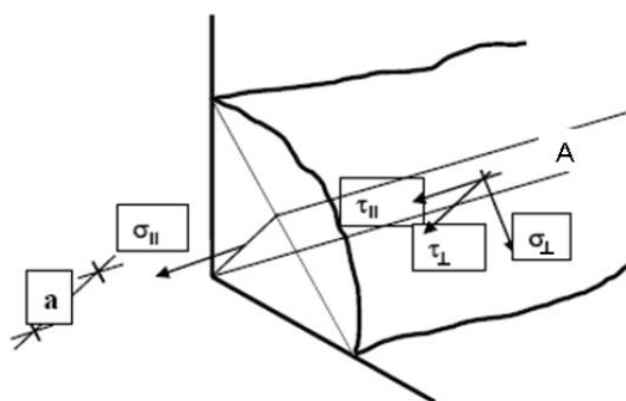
Plano de garganta de un cordón de soldadura.
